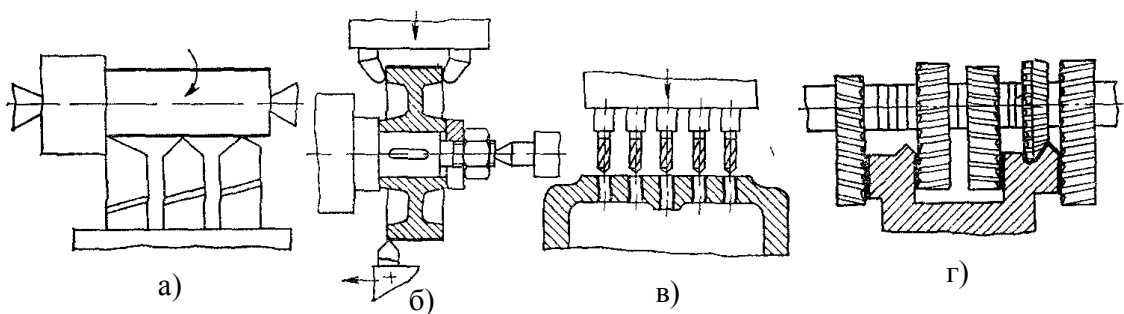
Схеми одномісної паралельної багатоінструментної обробки:
